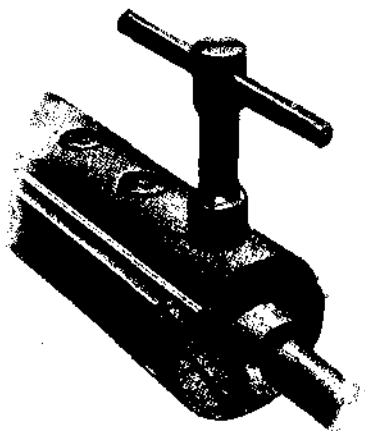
Конструкция ножевого вала, использующая центробежную силу для прочного закрепления ножей.
